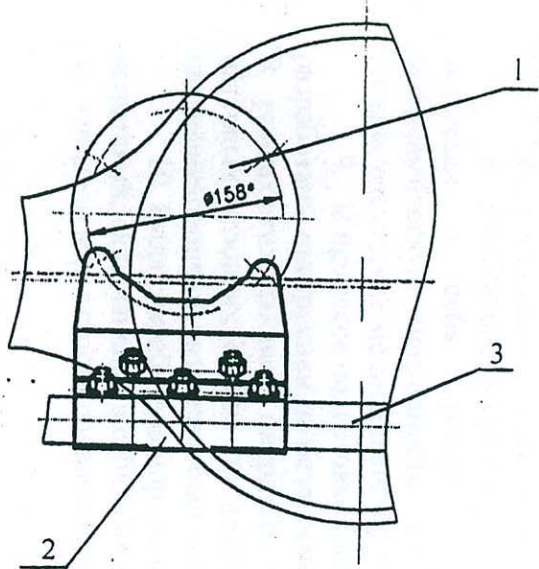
Колесо имитатора транспортного модуля. Общий вид
